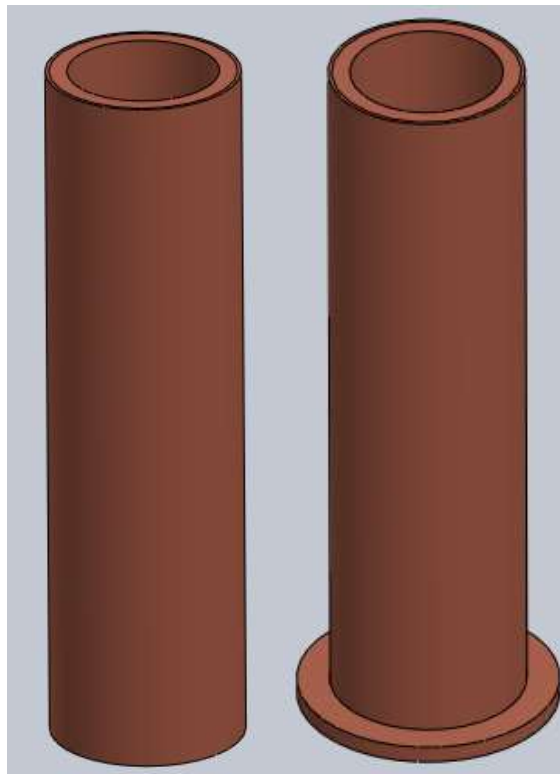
Buje de bronce (izquierda) y buje de bronce con tapa soldada (derecha).
